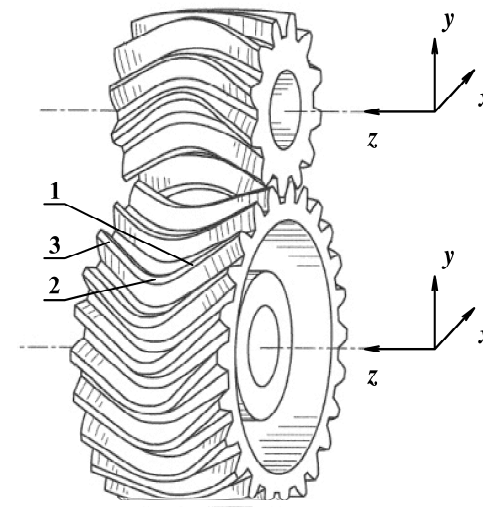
Цилиндрическая эвольвентная передача с арочно-винтовыми зубьями: 1, 3 - косозубые участки; 2 - арочный участок зуба
